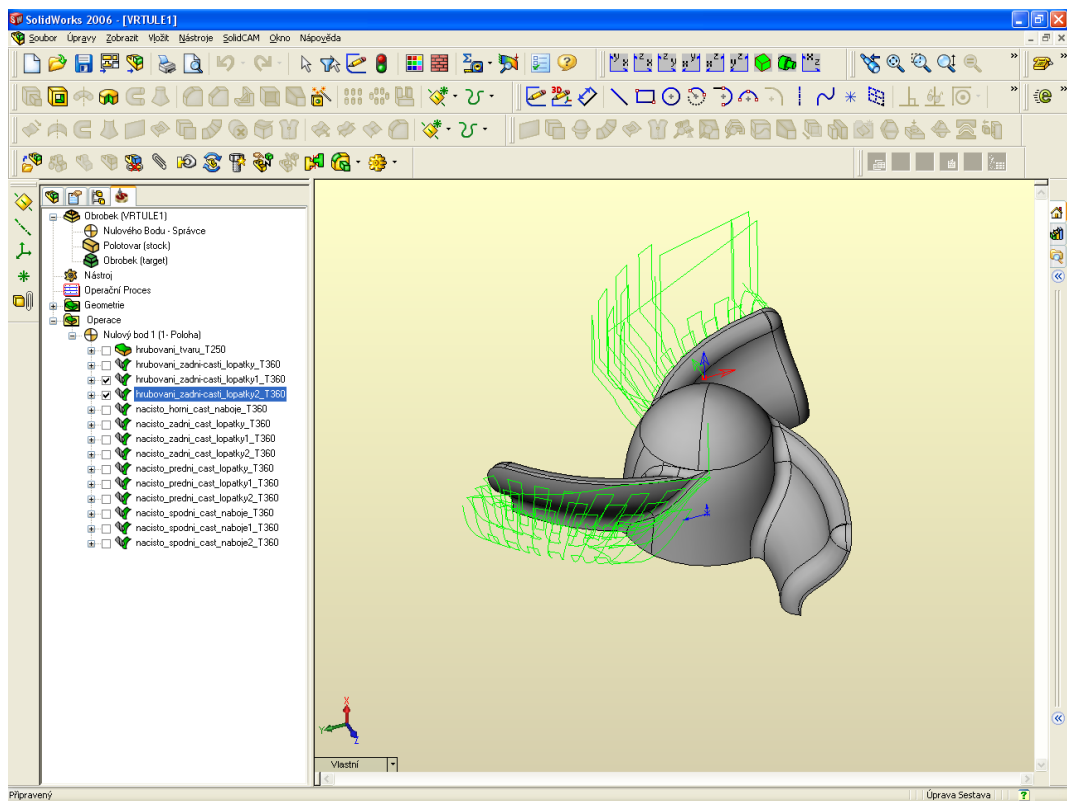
Operace hrubování tvaru Vrtule1 (SolidCAM R10)
